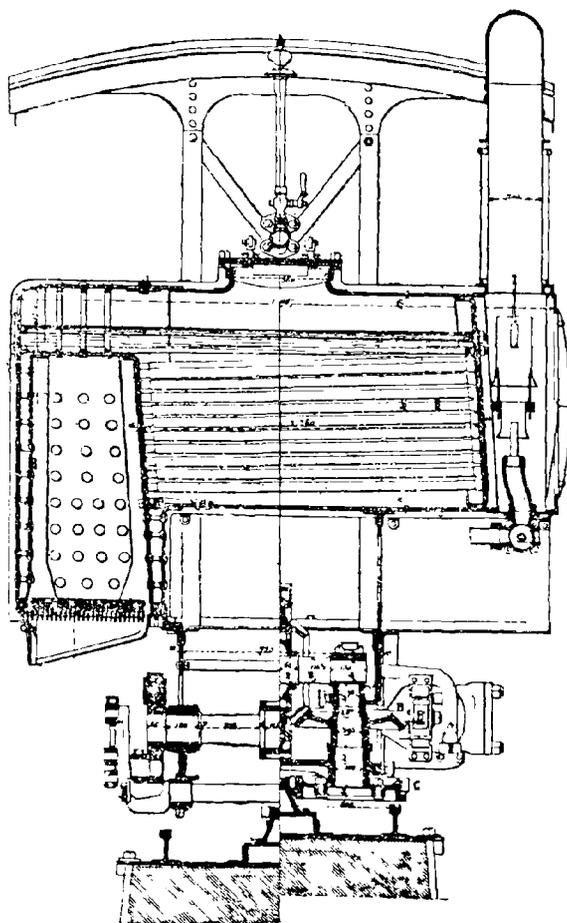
Coupe transversale de la machine du Mont-Pilate.
